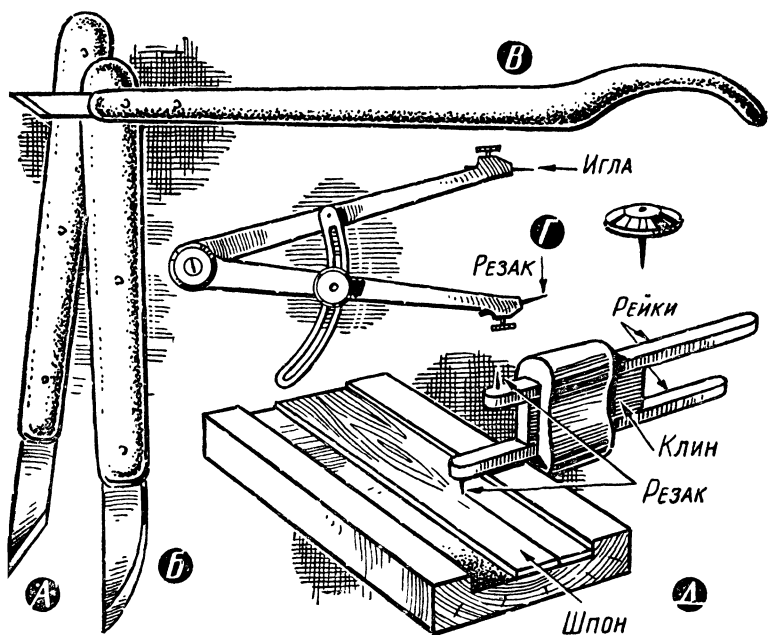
Инструмент для маркетри: А — прямой нож-резак; Б — нож с закругленным лезвием; В — плечевой резак; Г — циркуль-резак; Д — рейсмус-резак.
